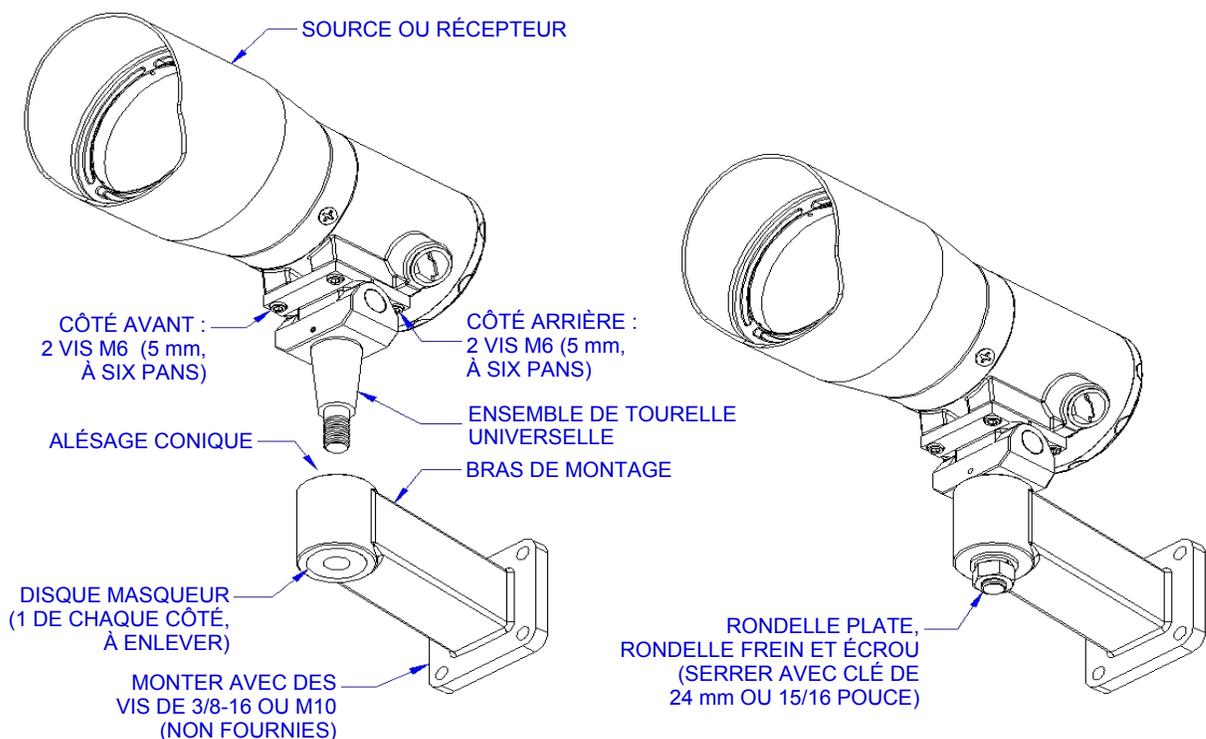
Dessin dimensionnel d'encombrement avec les options de montage
